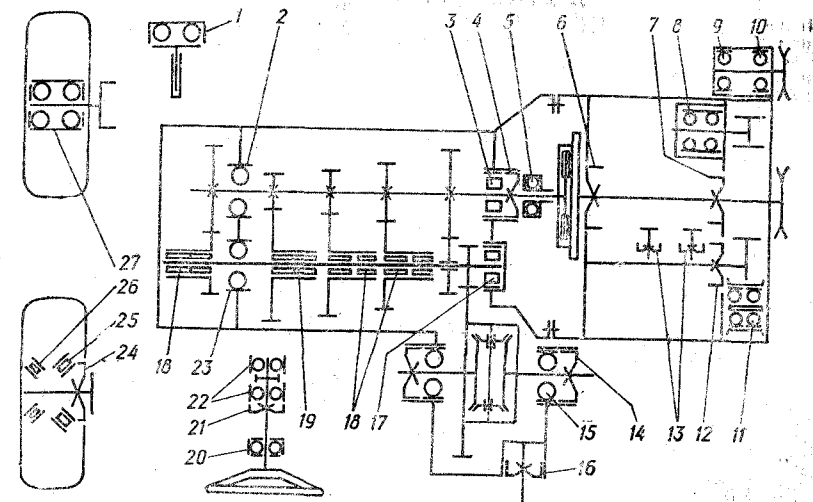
Схема расположения подшипников качения и манжетных уплотнителей (см. позиции в таблицах приложений 5 и 6)
